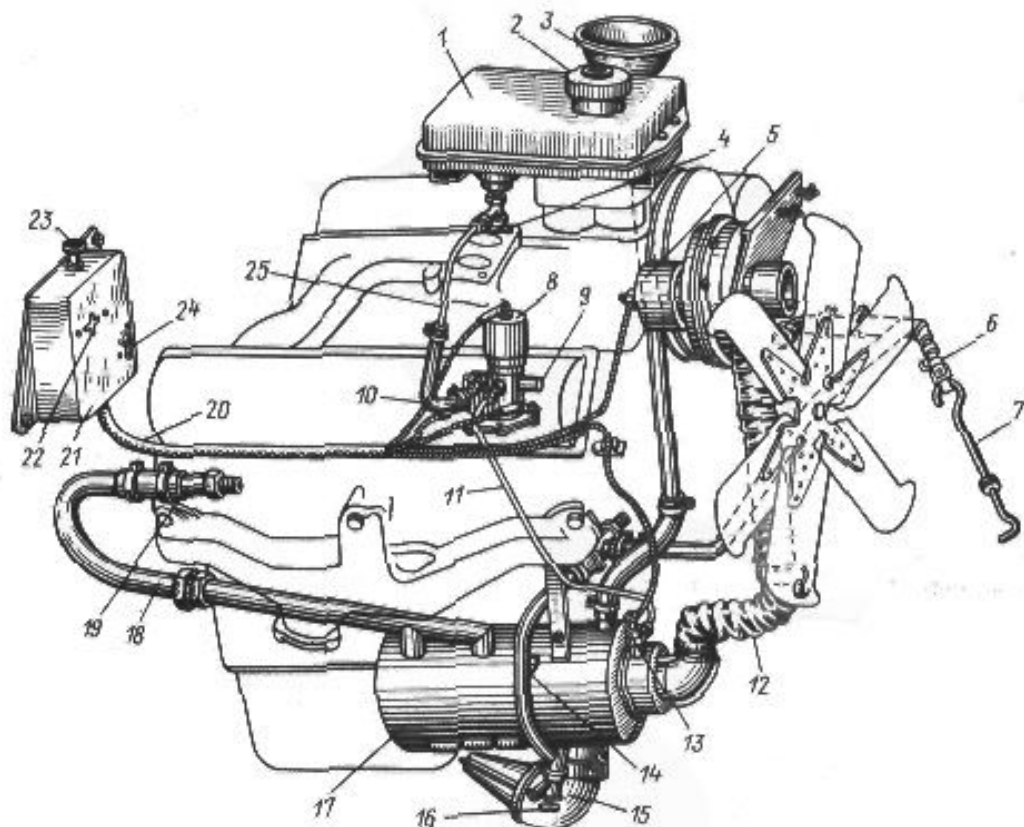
Предпусковой подогреватель двигателя автомобиля ЗИЛ-130
